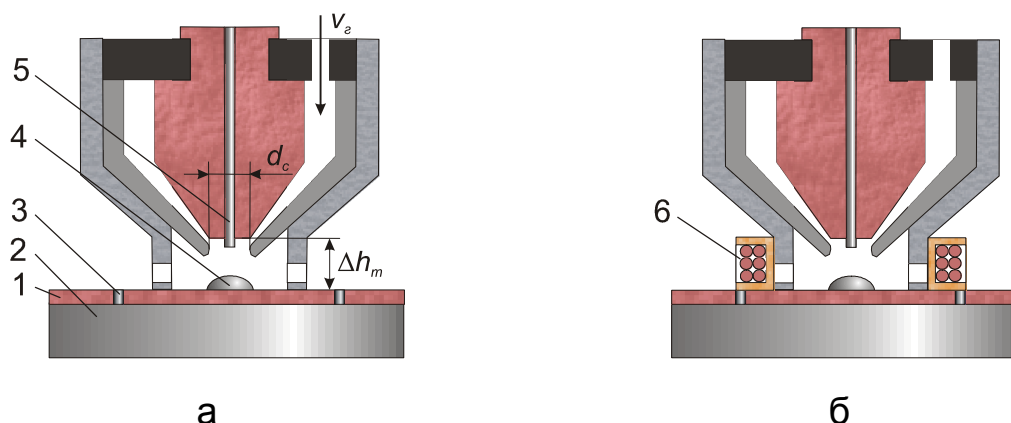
Схема стенда при определении точности нанесения металла: а – без закрутки магнитным полем; б – с закруткой магнитным полем
